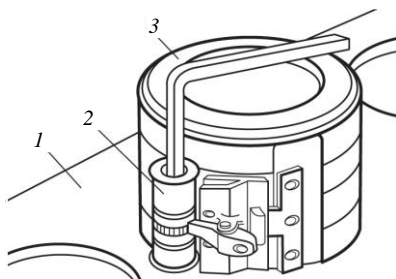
Установка поршня в гильзу с помощью ленточного приспособления: 1 – блок цилиндров; 2 – приспособление для сжатия поршневых колец; 3 – поршень
